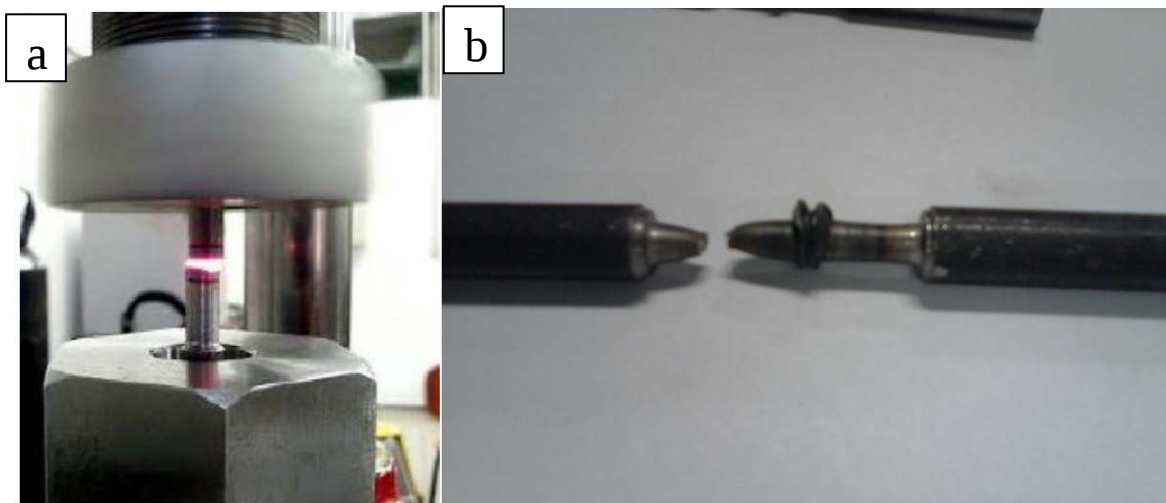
a. Solda realizada na máquina didática por solda a fricção - Figura 15.b. Corpo de prova rompido após uma carga de tração.
